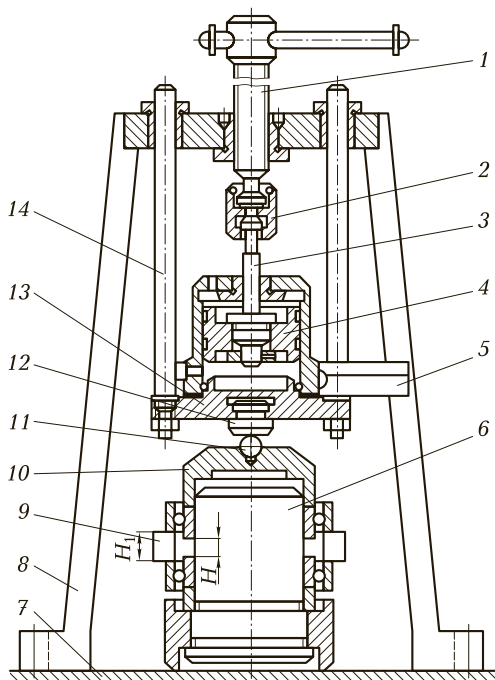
Приспособление для определения относительного смещения торцов колец подшипников:
